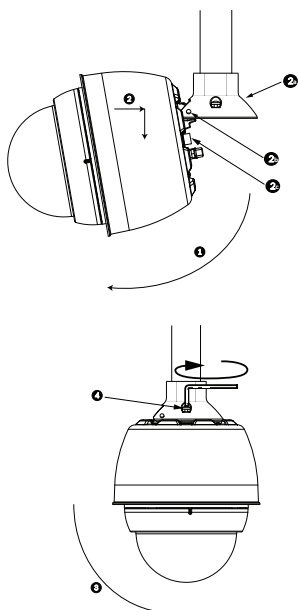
Montieren des Hängegehäuses an Dachbrüstungs-/Rohrhalterung
